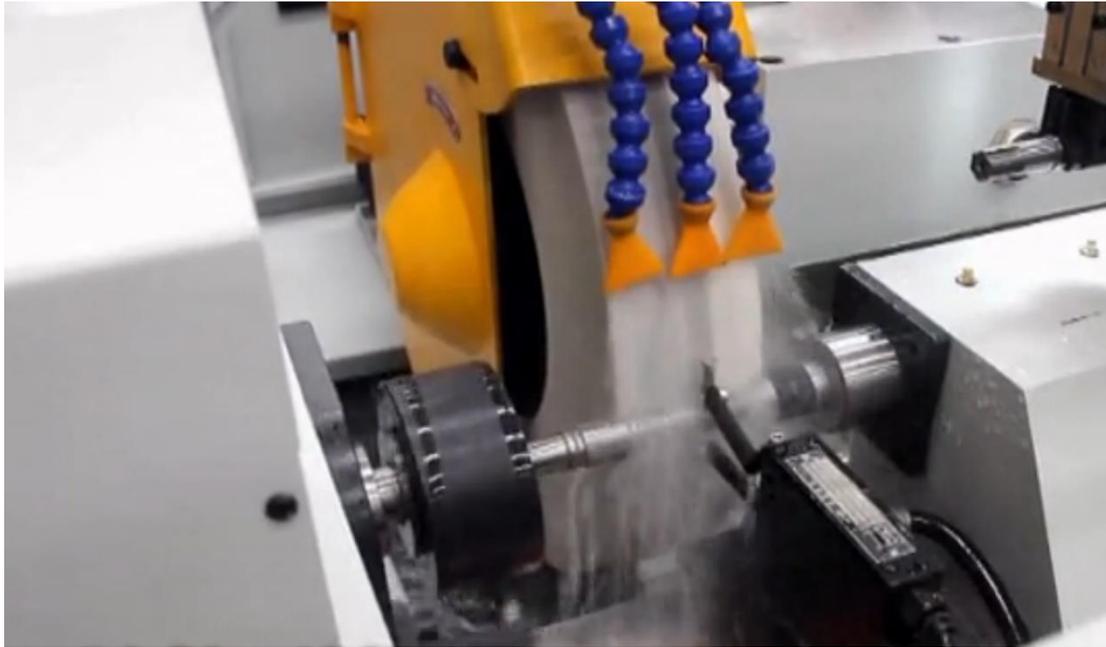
Bearbeitung mit CNC-Rundschleifmaschine^[13]
